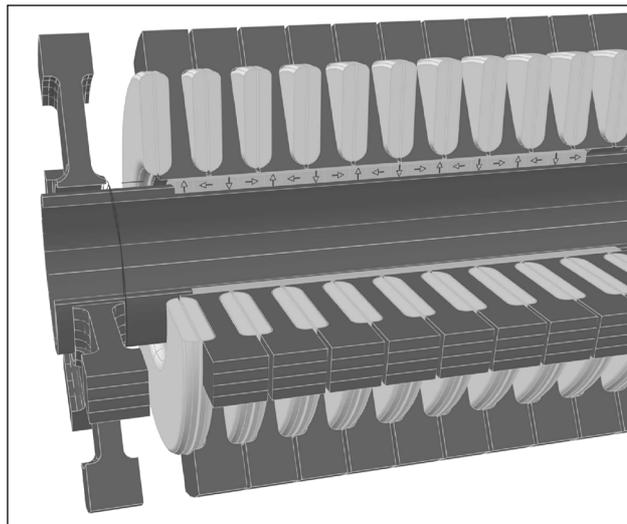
Сборка зубчатого статора цилиндрической линейной машины
